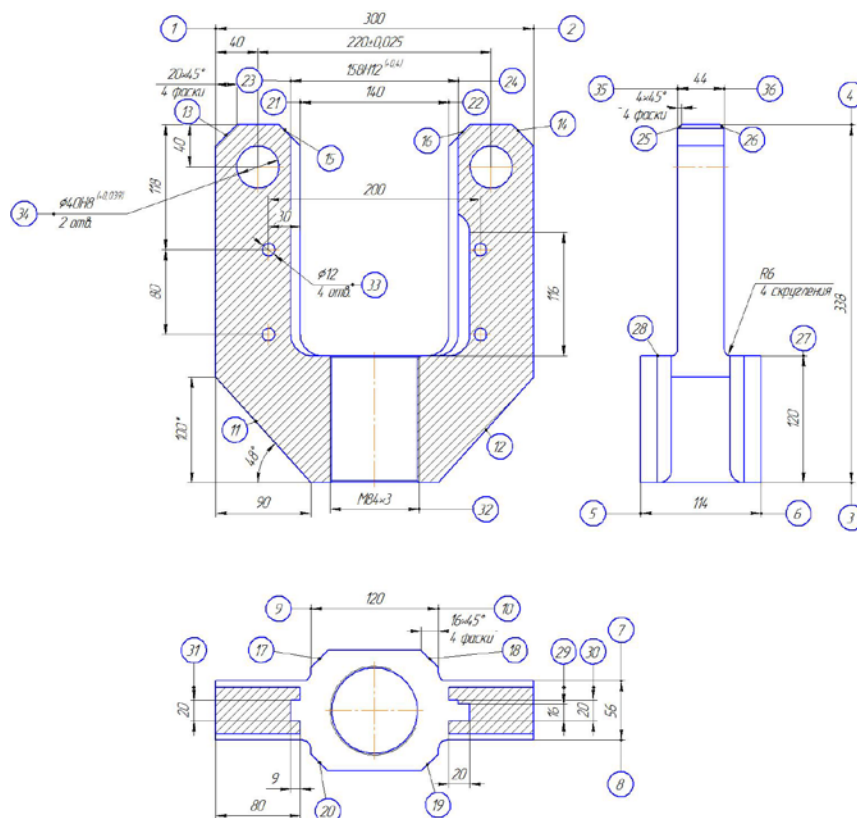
Эскиз детали с номерами обрабатываемых поверхностей
